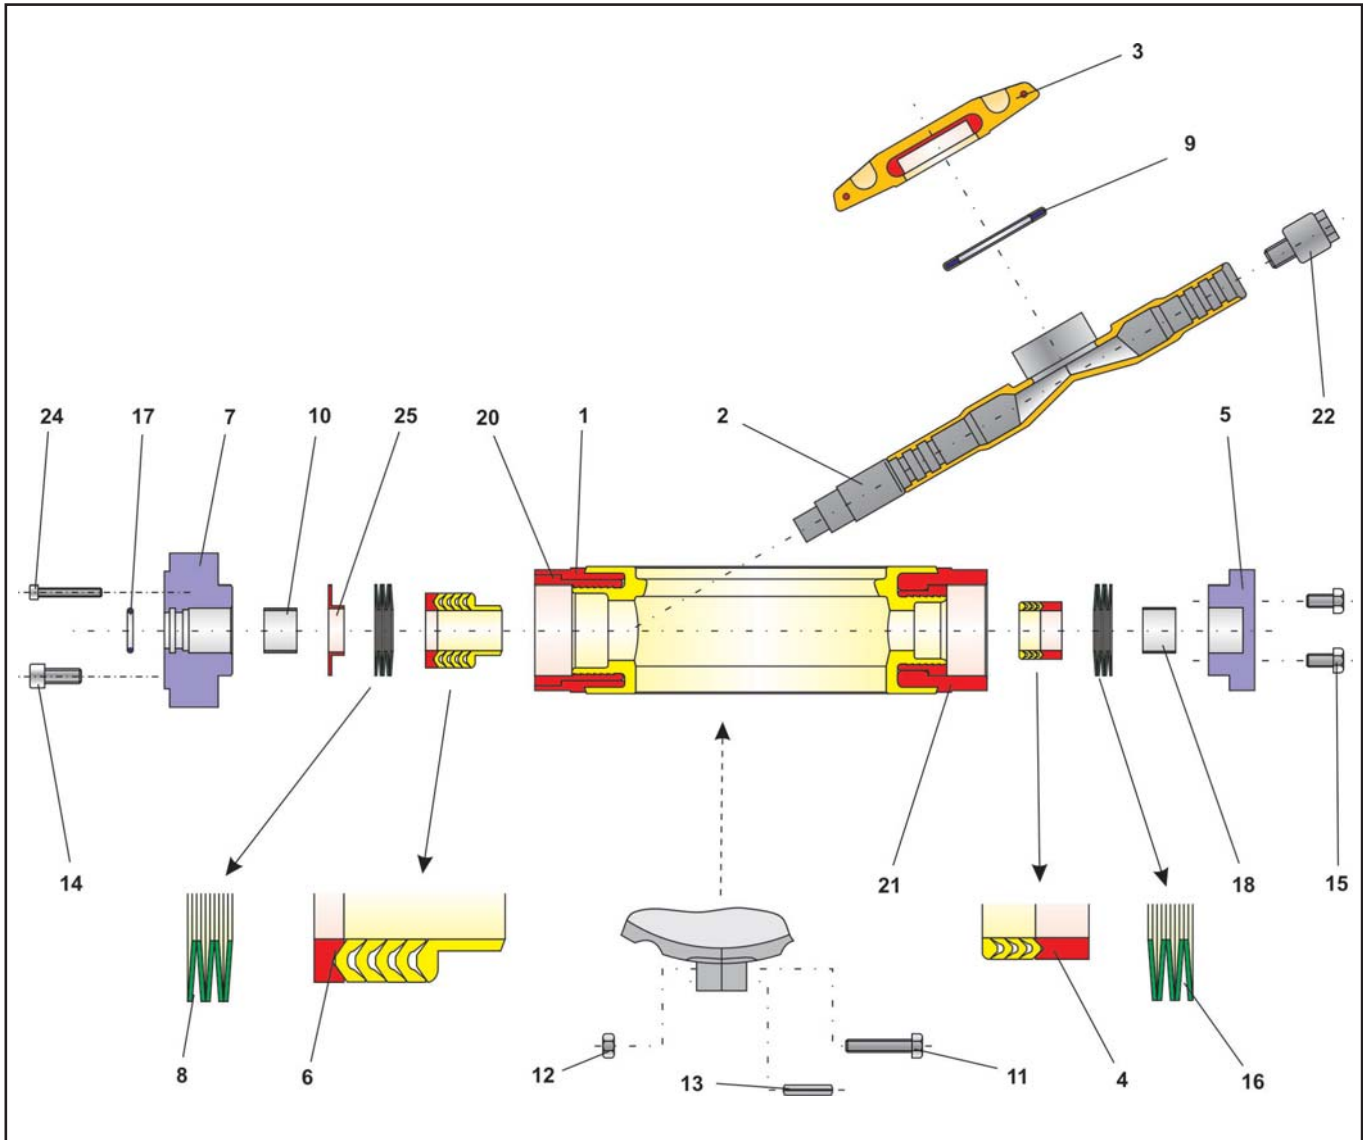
Explosionszeichnung der Stellklappe mit nachstellbarer Stopfbuchse BR 10a
